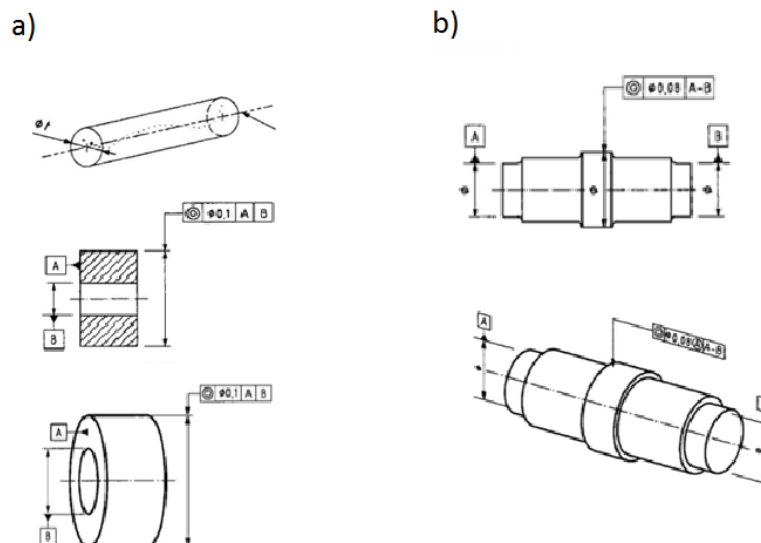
Zobrazení tolerančního pole soustřednosti bodu [3]
